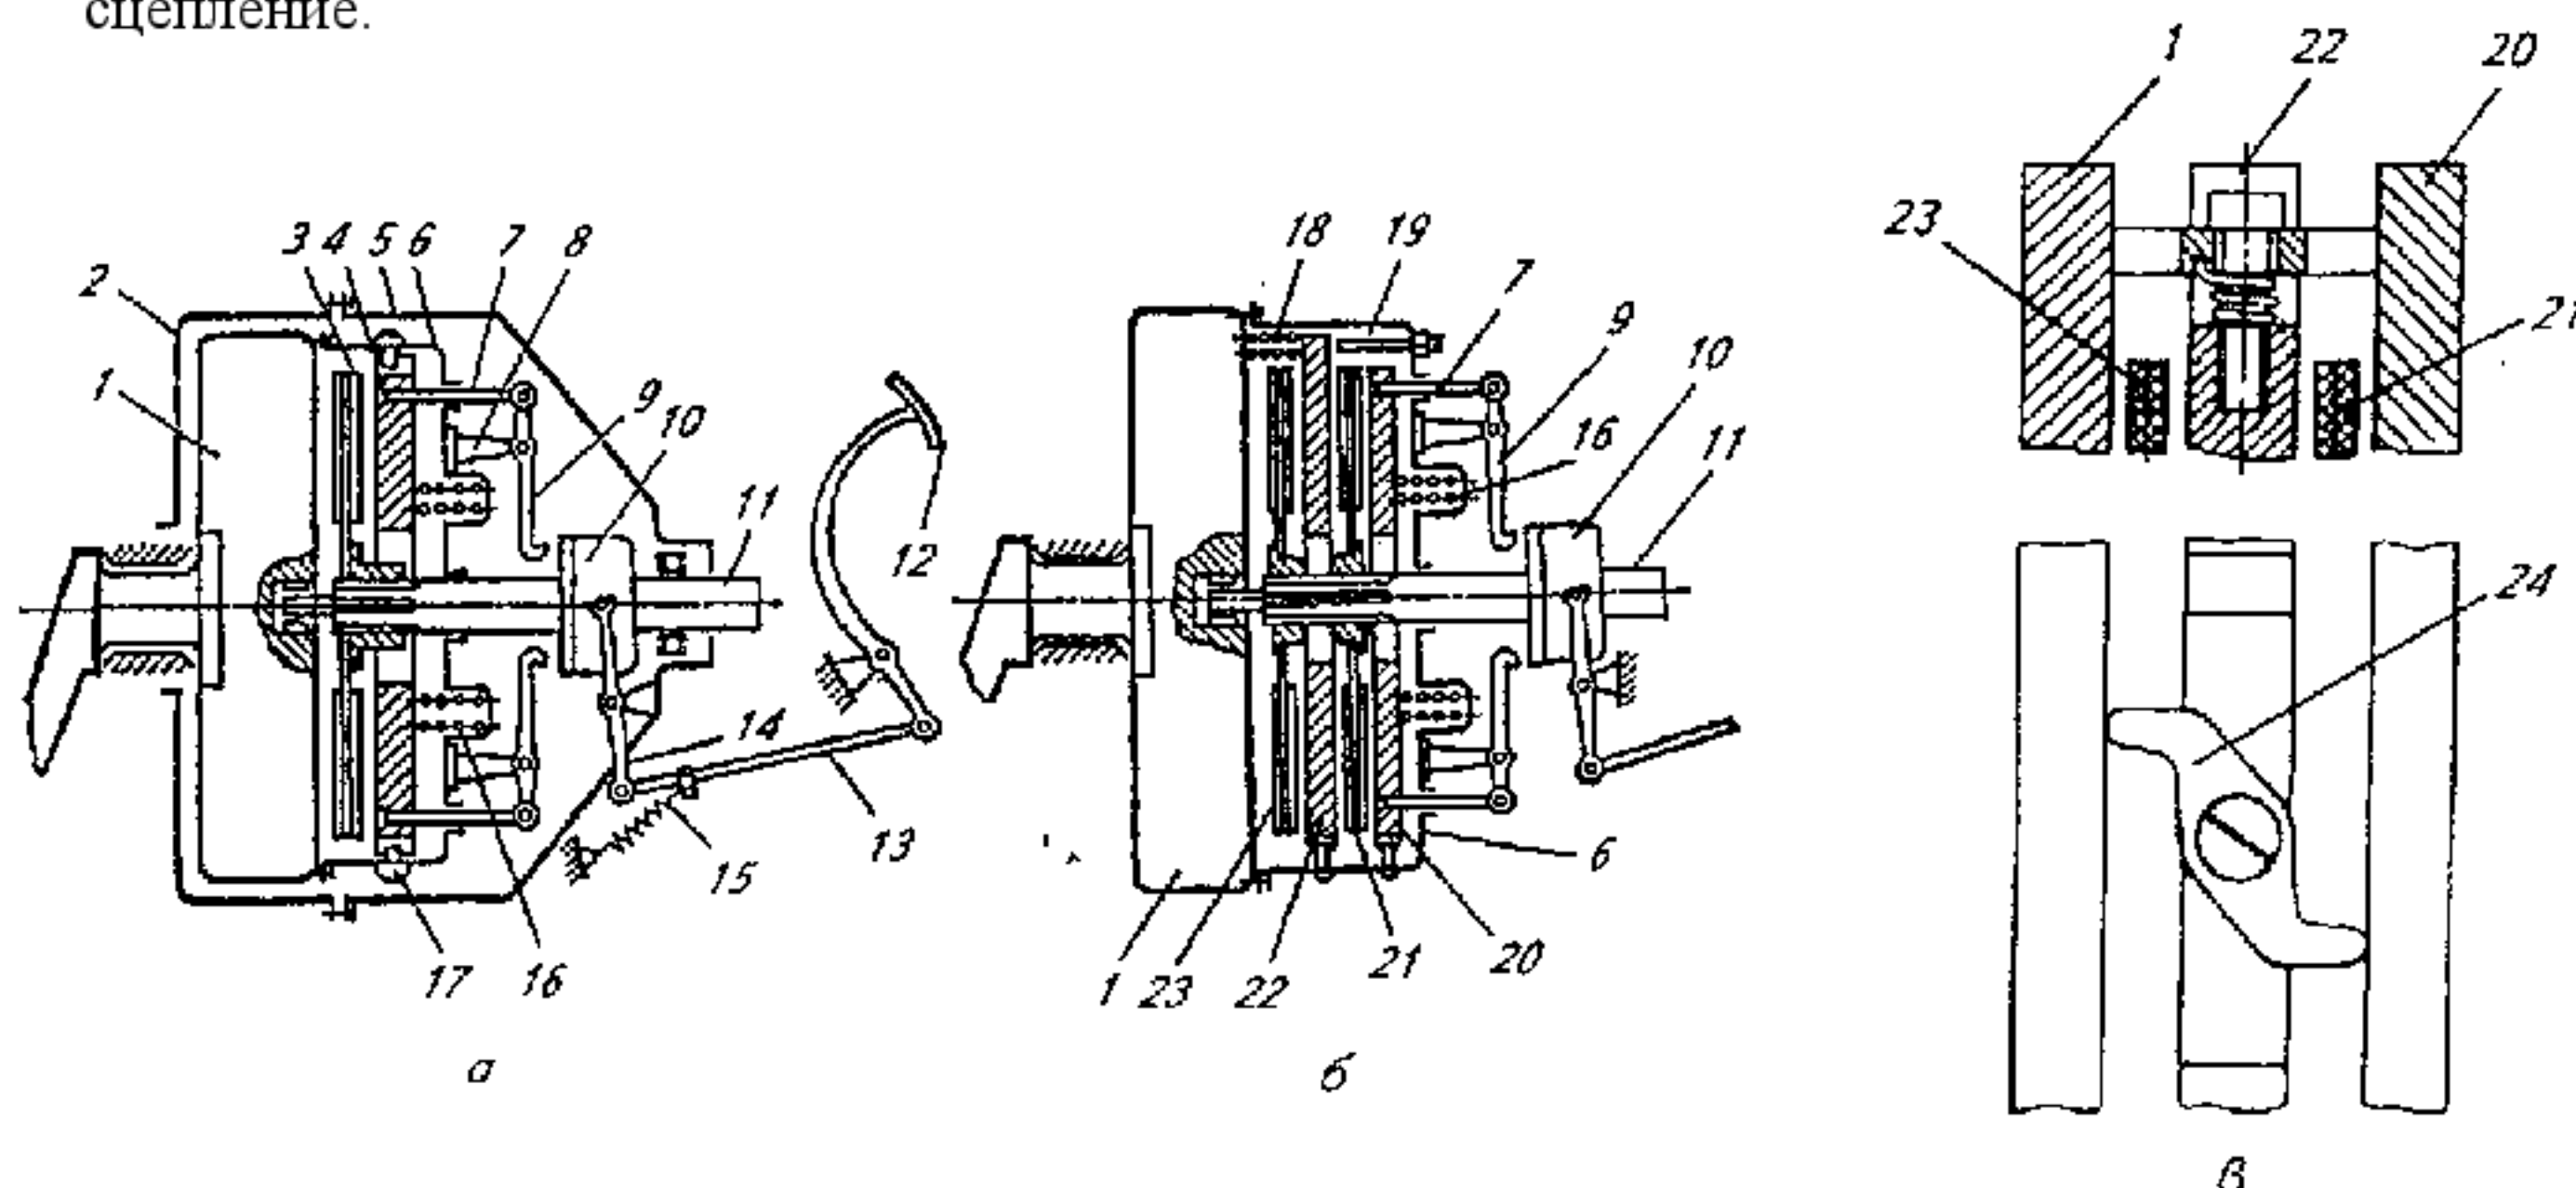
Схемы механических постоянно замкнутых сцеплений: а — однодискового; а — двухдискового; в — раздвижная скоба; 1 — маховик; 2 — корпус маховика; 3 — ведомый диск; 4 — нажимной диск; 5 — корпус сцепления; 6 — кожух; 7 — тяга; 8 — опоры отжимных рычагов; 9 — отжимные рычаги; 10 — выжимной подшипник; 11 — вал сцепления; 12 — педаль; 13 — тяга; 14 — вильчатый рычаг; 15 — оттяжная пружина; 16 — нажимные пружины; 17 — ведущие пальцы; 18 — отжимная пружина среднего нажимного диска; 19 — болт-ограничитель хода среднего нажимного диска; 20 — задний нажимной диск; 21 — задний ведомый диск; 22 — средний нажимной диск; 23 — передний ведомый диск; 24 — раздвижная скоба
